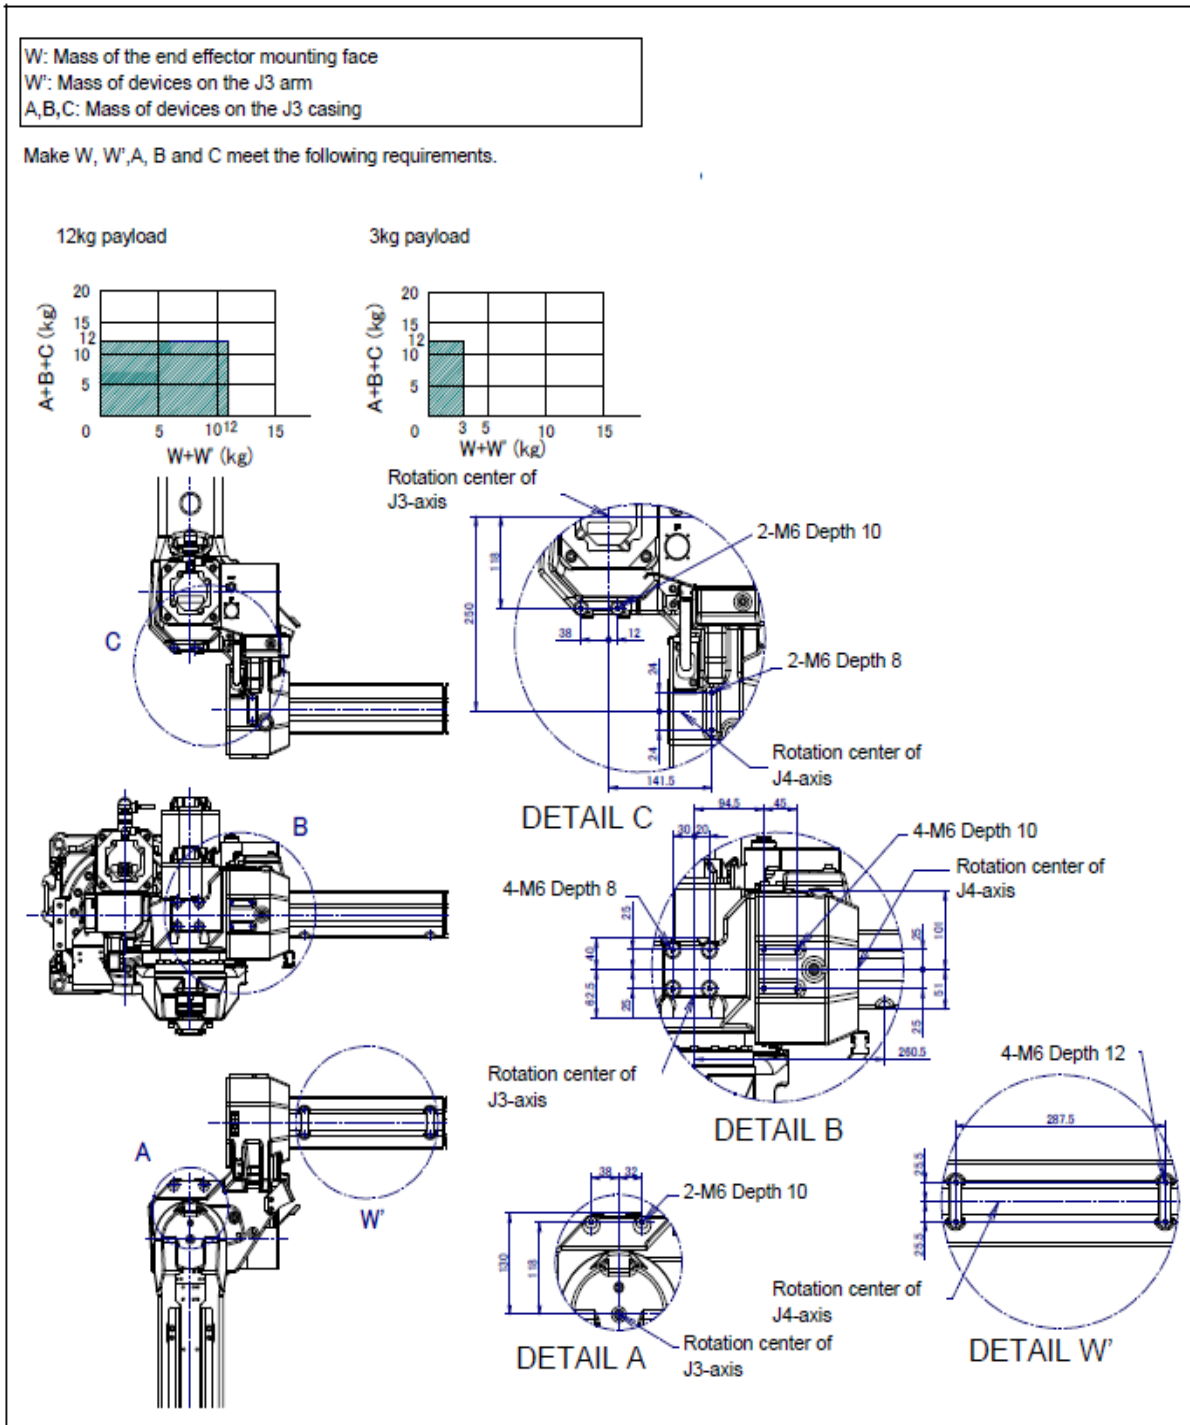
(b) Surfaces de montage d'équipement (ARC Mate 120iC/12L, M-20iA/12L)
